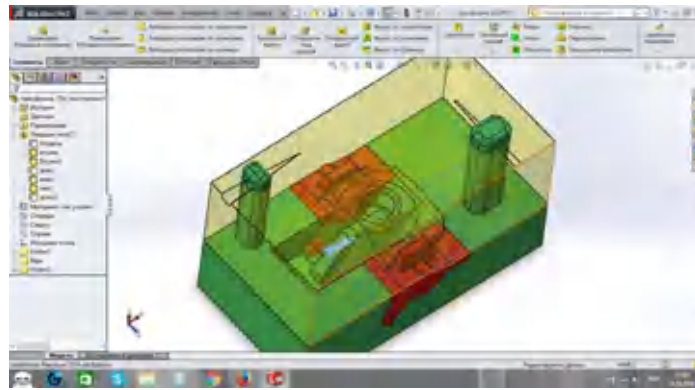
3D-пресс-форма лиття восковок в сборе
